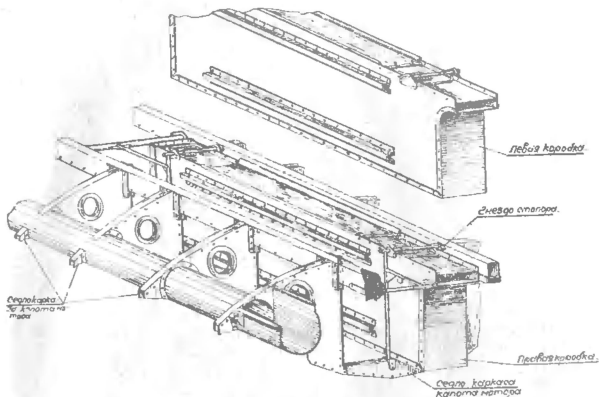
Установка патронных коробок пулемета «ШКАС».
